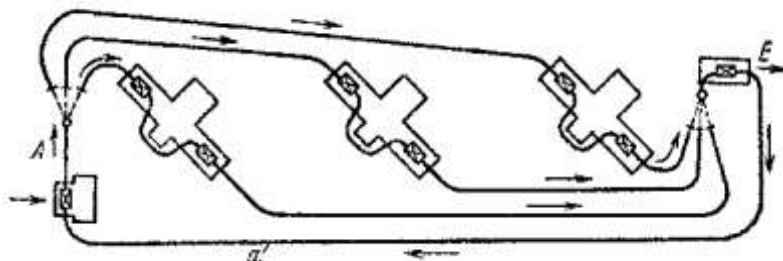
Монорельсовый путь для подачи деталей к станкам
